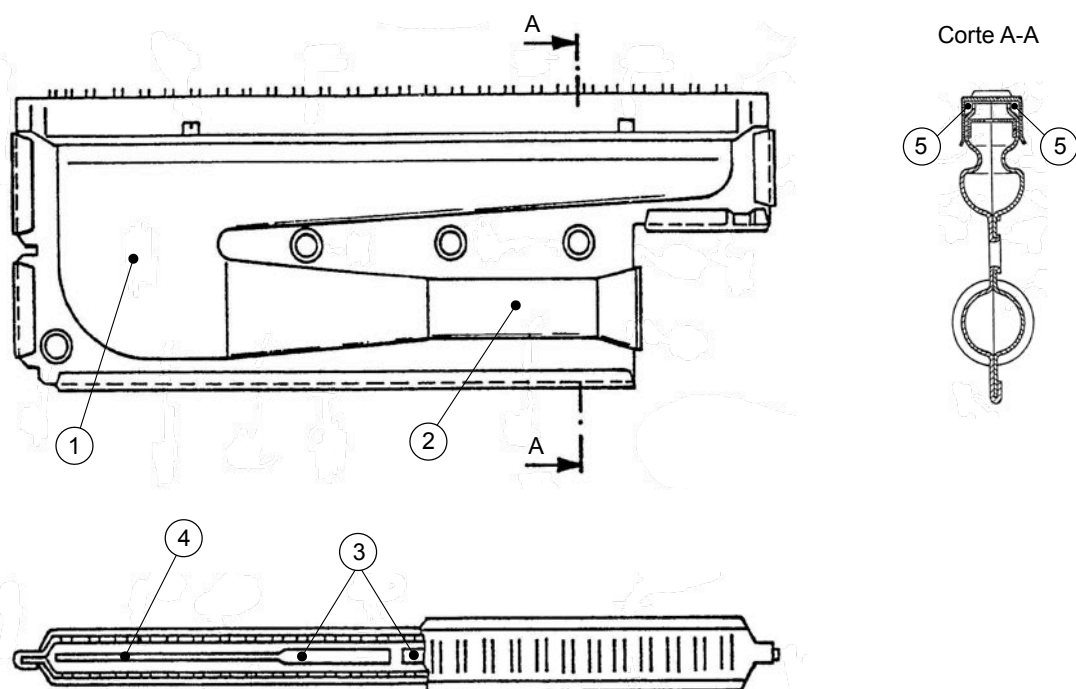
Esquema ilustrativo da flauta: *alçado principal, vista de cima e vista em corte* (Adaptado de Seebauer, 1981)
